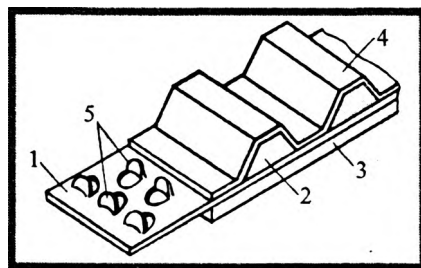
Зубчатый ремень с несущим слоем в виде металлической ленты:
